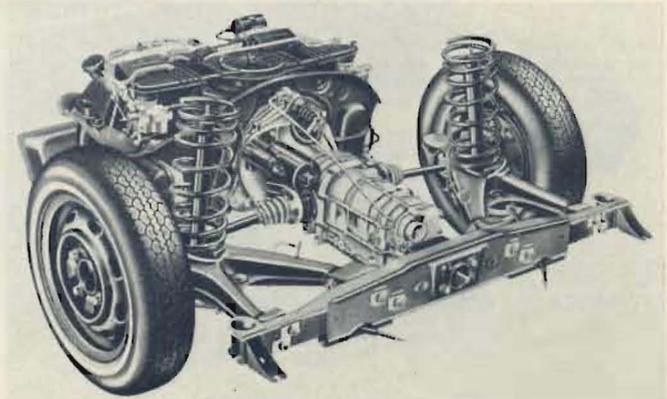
Hinterachsaggregat mit neuem Motor und neuem Getriebe; Schräglenkerachse, progressive Federung mit Schrauben- und Gummifeder
